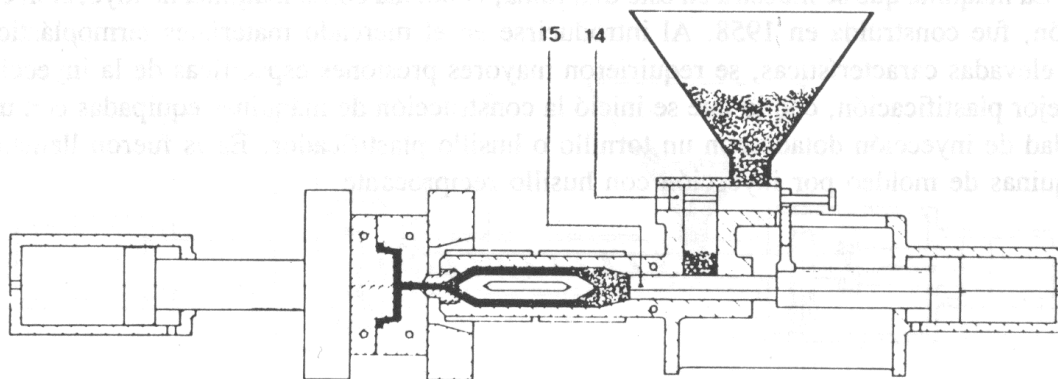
Diagrama simplificado de una máquina de moldeo por inyección tipo pistón. Nótese que el molde está cerrado y el pistón (15) se encuentra en la fase final de la inyección, mientras que el dosificador (14) ha terminado la alimentación del material.
